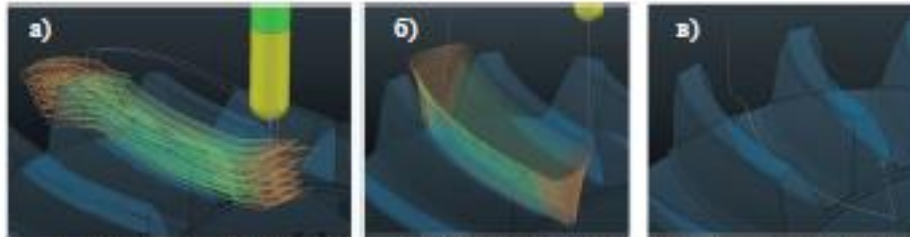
Траектории перемещения концевой фрезы а) черновом фрезеровании впадины, б) при чистовом фрезеровании, в) при обработке дна впадины зубчатого колеса.
